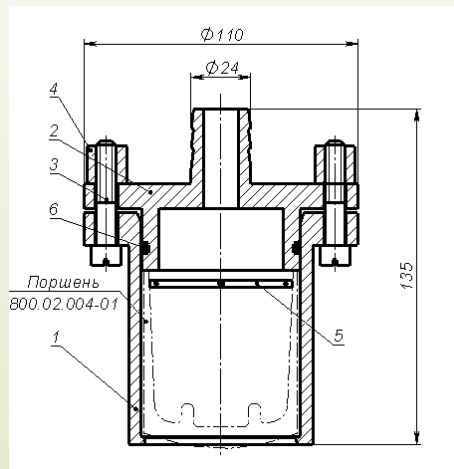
Конструкция опытного образца приспособления для МДО поршней
